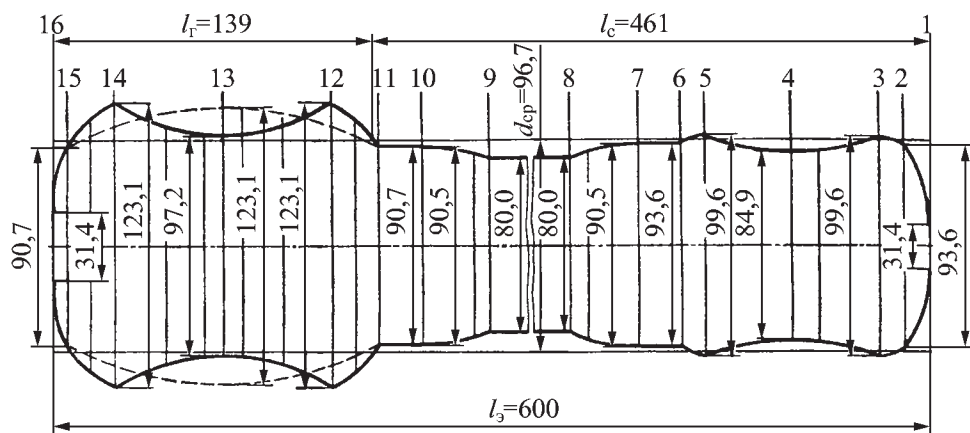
Расчетная заготовка поковки прицепного шатуна (эпюра диаметров)
